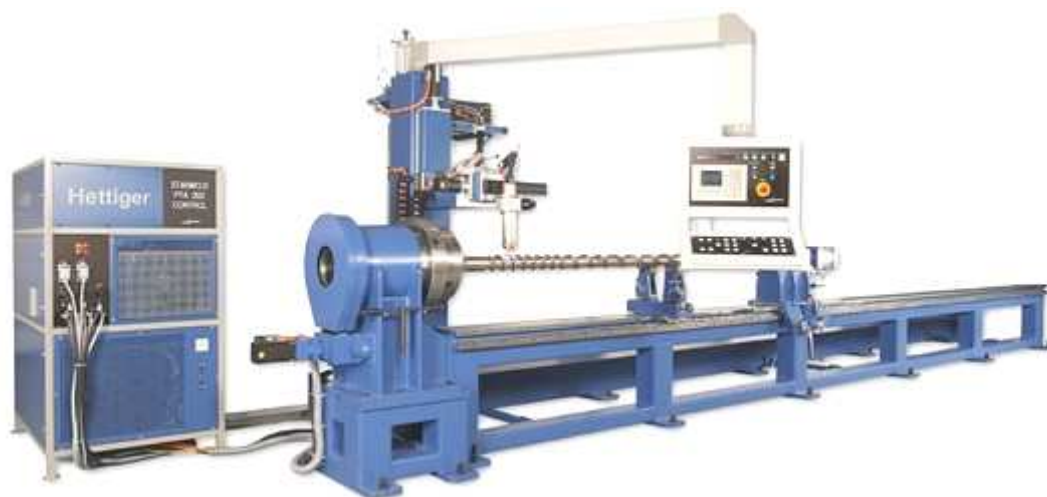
Фотография установки Coating Star III для плазменной наплавки поверхностей деталей
